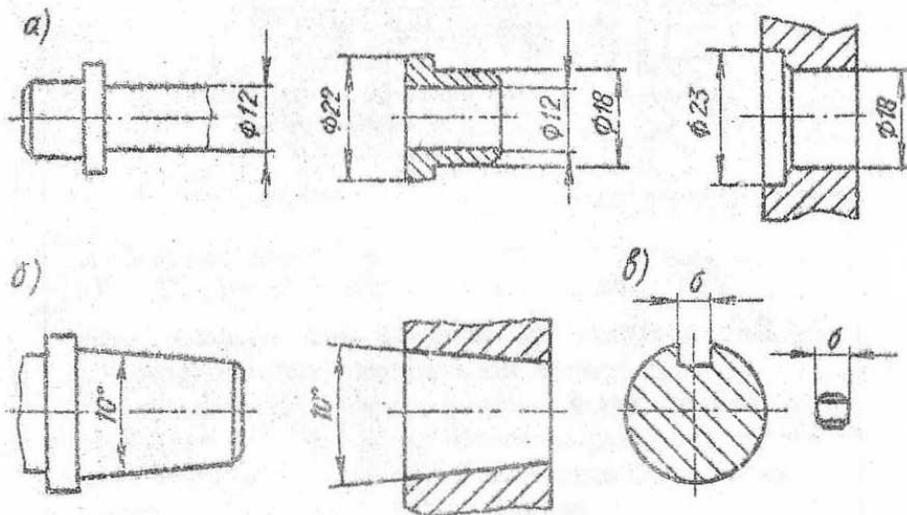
Размеры на чертежах деталей: а - для цилиндрических соединений; б - для конического соединения; в - для плоского соединения
